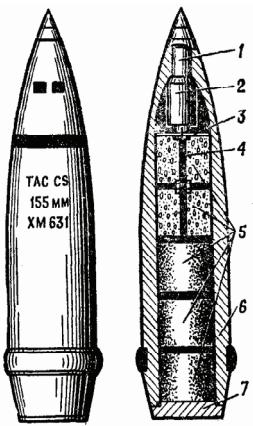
155-мм химический снаряд XM631: 1 – взрыватель; 2 – пороховой заряд; 3 – диафрагма; 4 – перфорированная трубка; 5 – шашки с отправляющим веществом; 6 – корпус; 7 – дно снаряда
